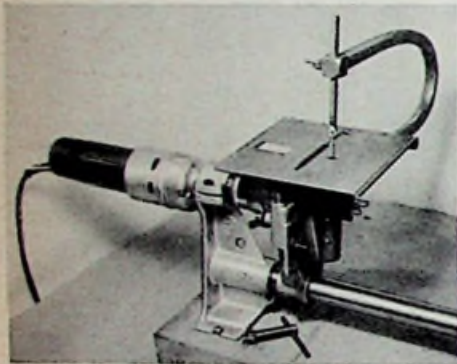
Dekupiersäge zum Bosch-Combi-Werkzeug
